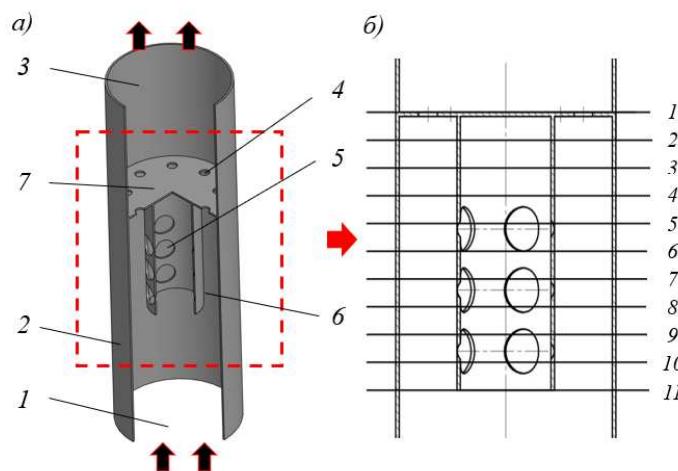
а) Упрощенная модель центробежного сепаратора с коаксильными цилиндрами: 1 – вход в устройство; 2 – наружный цилиндр; 3 – выход из устройства; 4 – массив круглых отверстий; 5 – отверстия для завихрения газа; 6 – внутренний цилиндр; 7 – перегородка с отверстиями; б) Расположение плоскостей для исследования окружных скоростей
